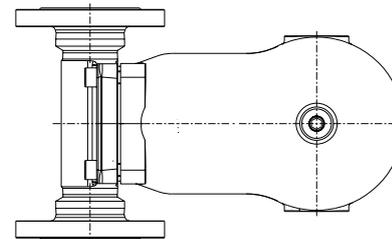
1 mit Flanschen - horizontale Einbaulage
